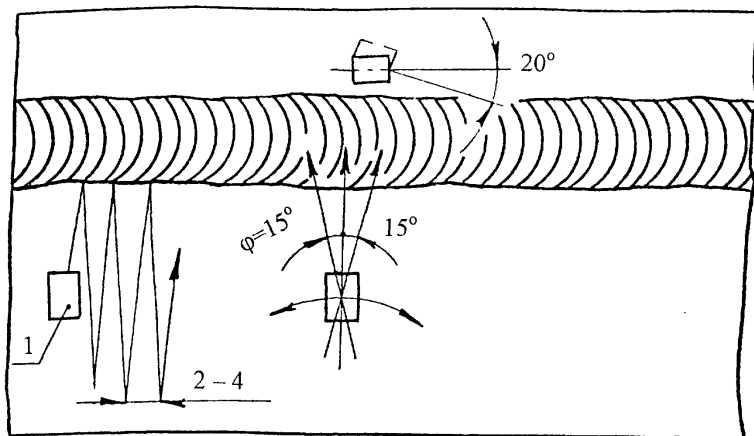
Схемы прозвучивания сварных соединений
